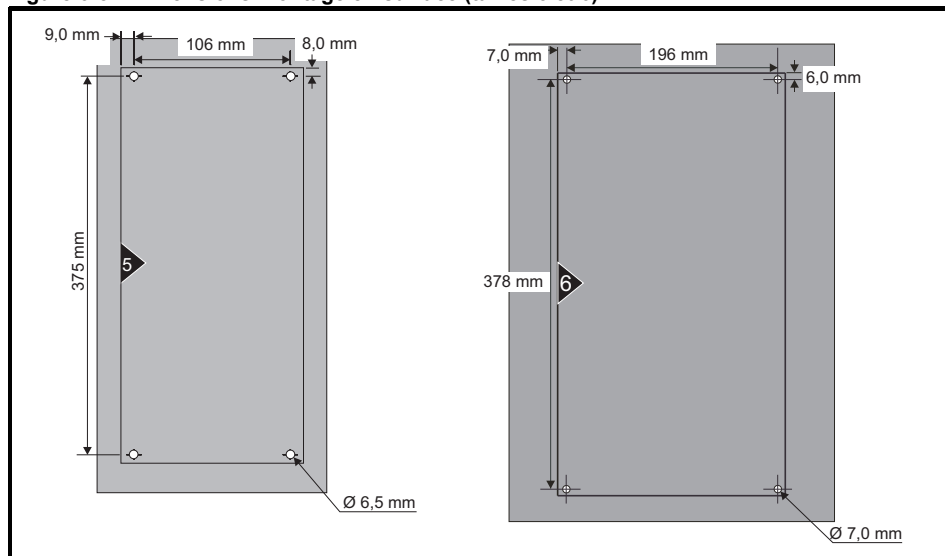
Dimensions du variateur (taille 5 illustrée)
